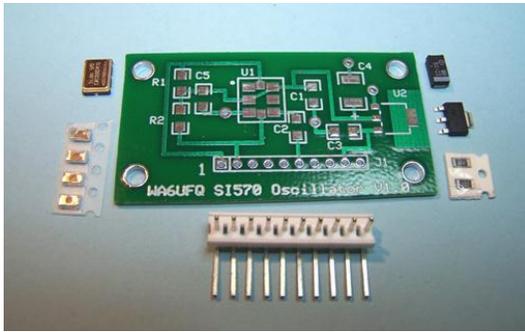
Modulo Si570 da assemblare ed assemblato
